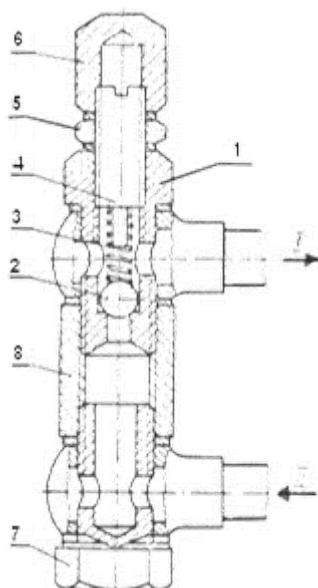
Клапан редукційний: 1 – ніпель, 2 – кулька, 3 – пружина, 4 – гвинт регулювальний, 5 – контргайка, 6 – гайка ковпачкова, 7 – ніпель, 8 – корпус. I – відвід палива при відкритті клапана, II – підведення палива
